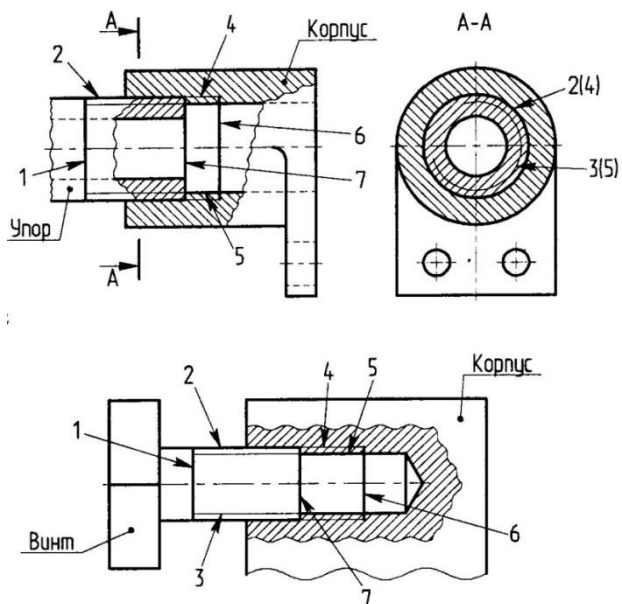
Резбовое соединение: 1 – граница резьбы на упоре (винте);
